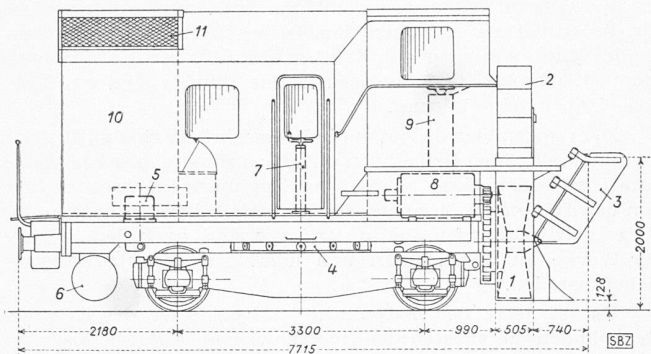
Typenbild 1:100 der elektrischen Schneeschleuder der SBB. 1 Schleuderrad, 2 Lenkschaufel, 3 Leitbleche, 4 Rollenkrantz zum Drehen des Kastens, 5 Hebezyliner, 6 Druckluftbehälter, 7 Handbremse, 8 Schleudermotor, 9 Regulierkontroller, 10 Kabine mit Hauptschalter und Stufentransformator, 11 Widerstände
